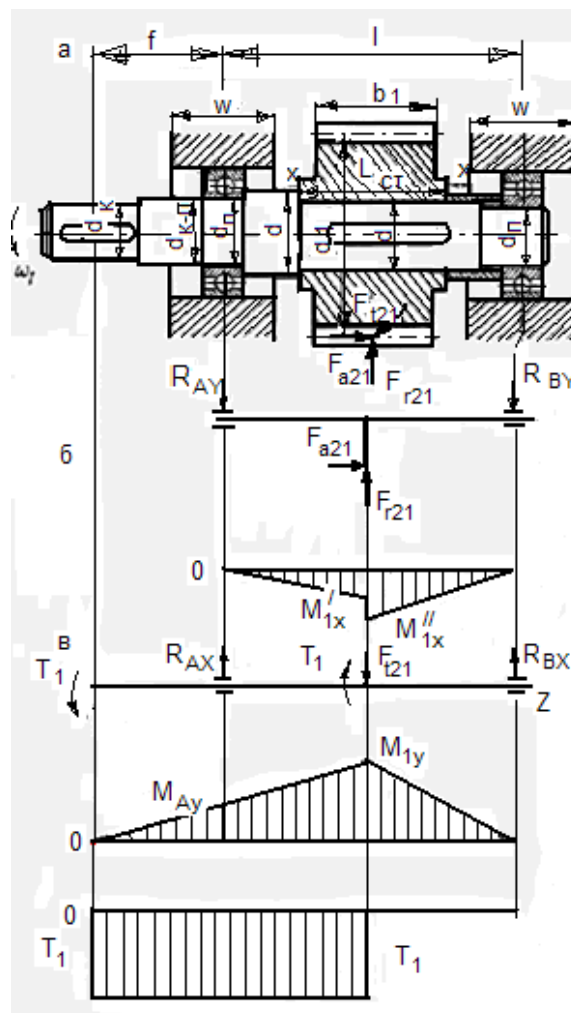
Схема ведущего вала цилиндрического косозубого редуктора:
